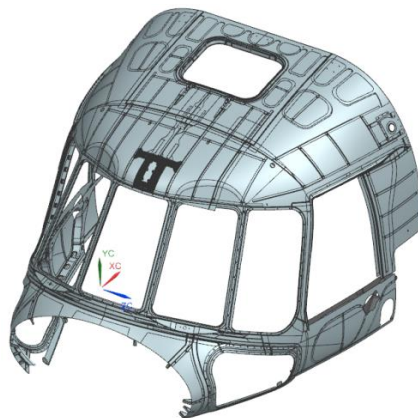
Внешний вид каркаса фонаря кабины пилотов вертолета Ми-171
